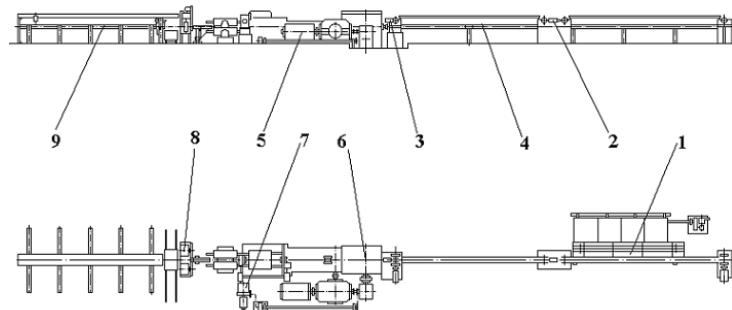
Схема стана холодної пилигримової прокатки труб
